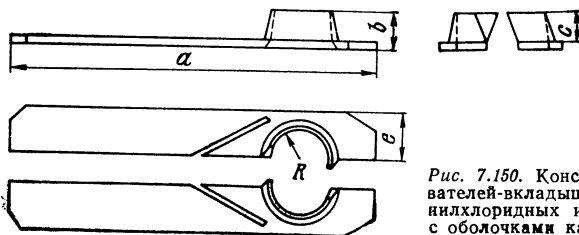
Конструкция медных нагревателей-вкладышей для сварки поливинилхлоридных и полиэтиленовых муфт с оболочками кабелей ТПВ и ТПП
